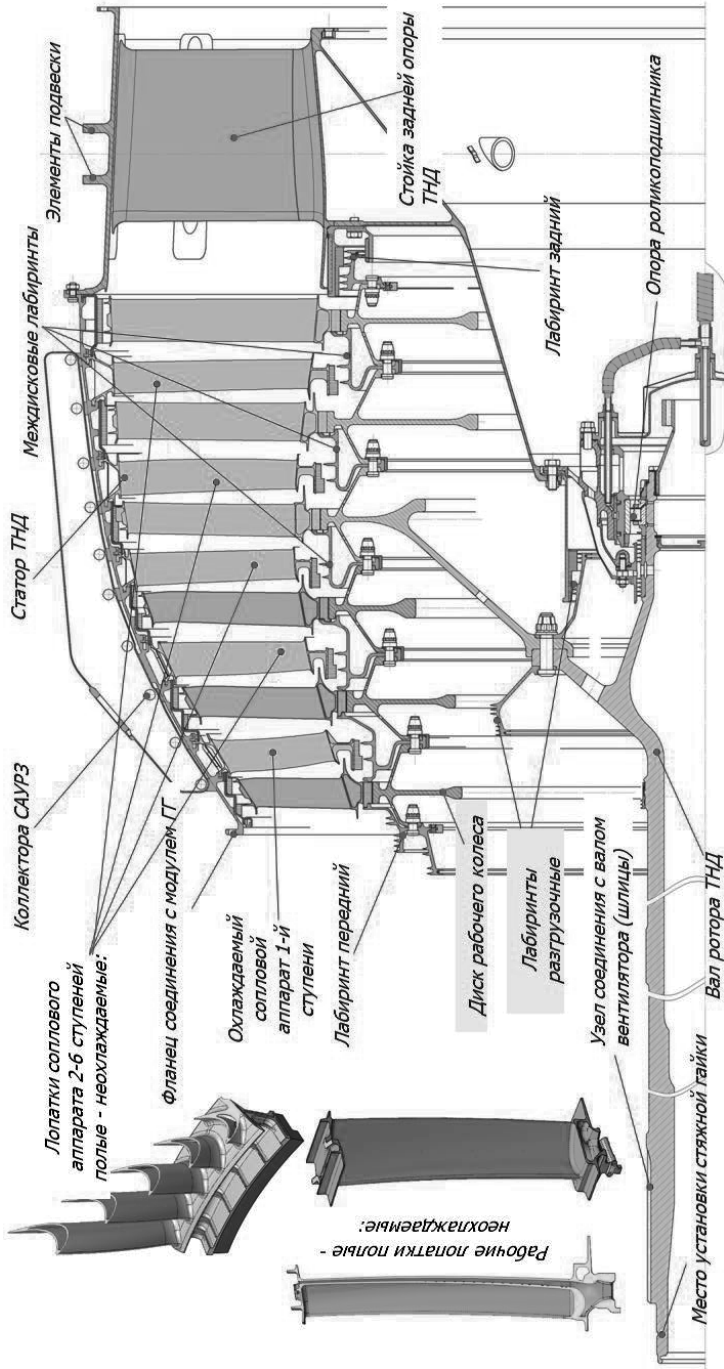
Схема модуля ТНД, рабочие лопатки и СА ТНД
